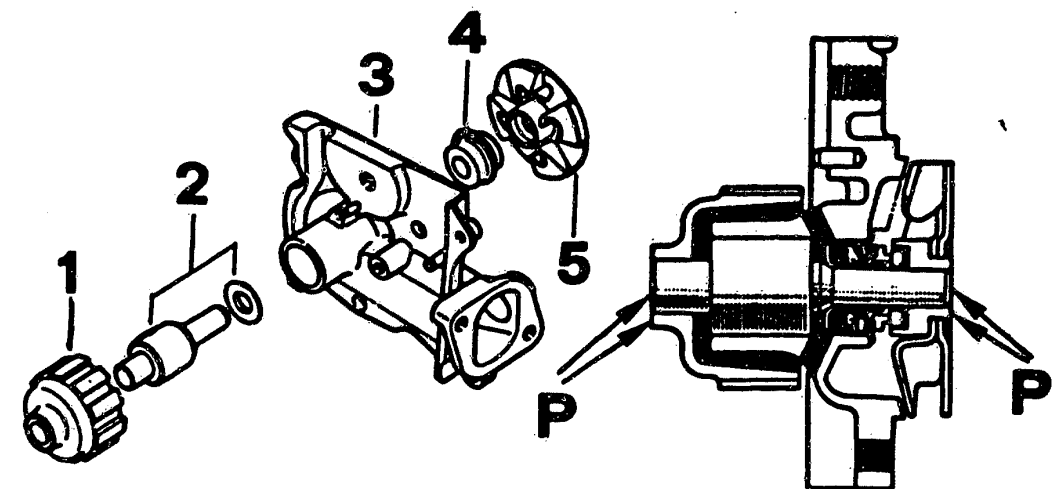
Einzelteile der Wasserpumpe. Die Flächen P (Pfeile) müssen jeweils plan sein. 1 Antriebsrad – 2 Welle – 3 Gehäuse – 4 Dichtung – 5 Pumpenrad.
